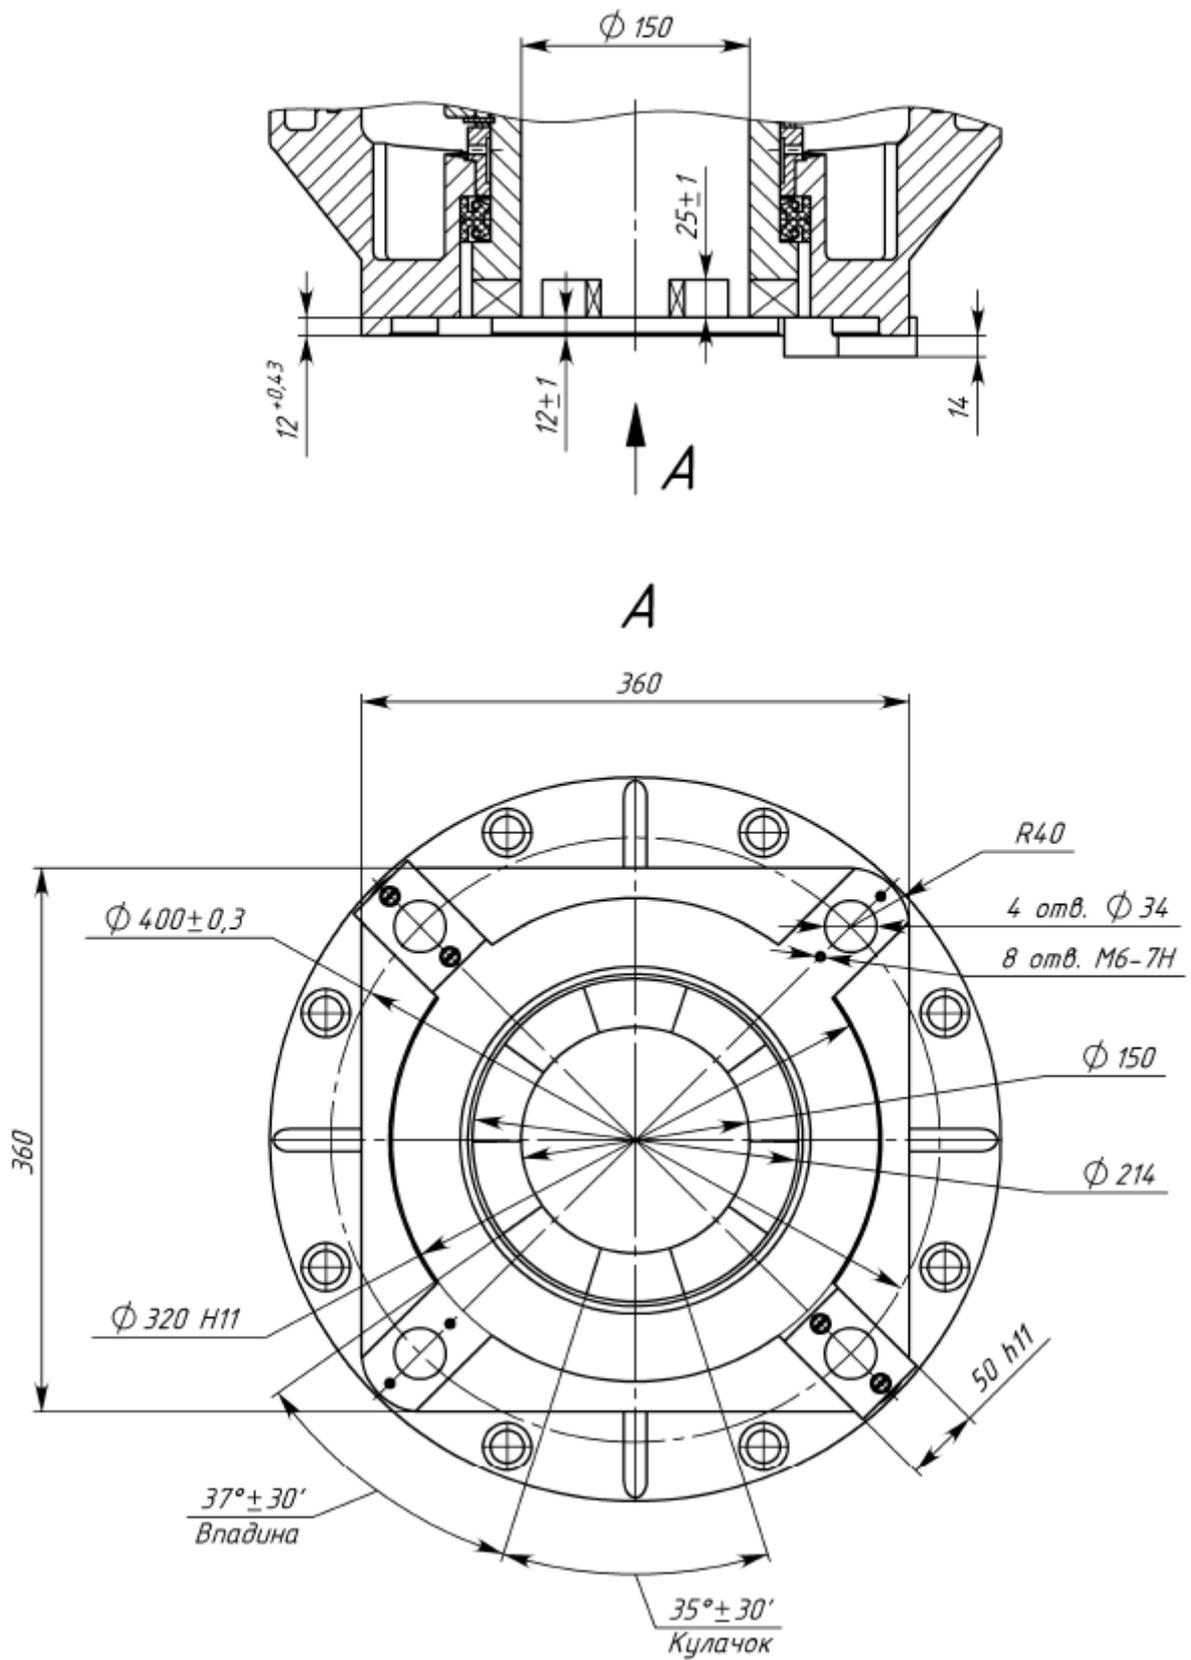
Присоединение типа Д для конструктивной схемы 44
